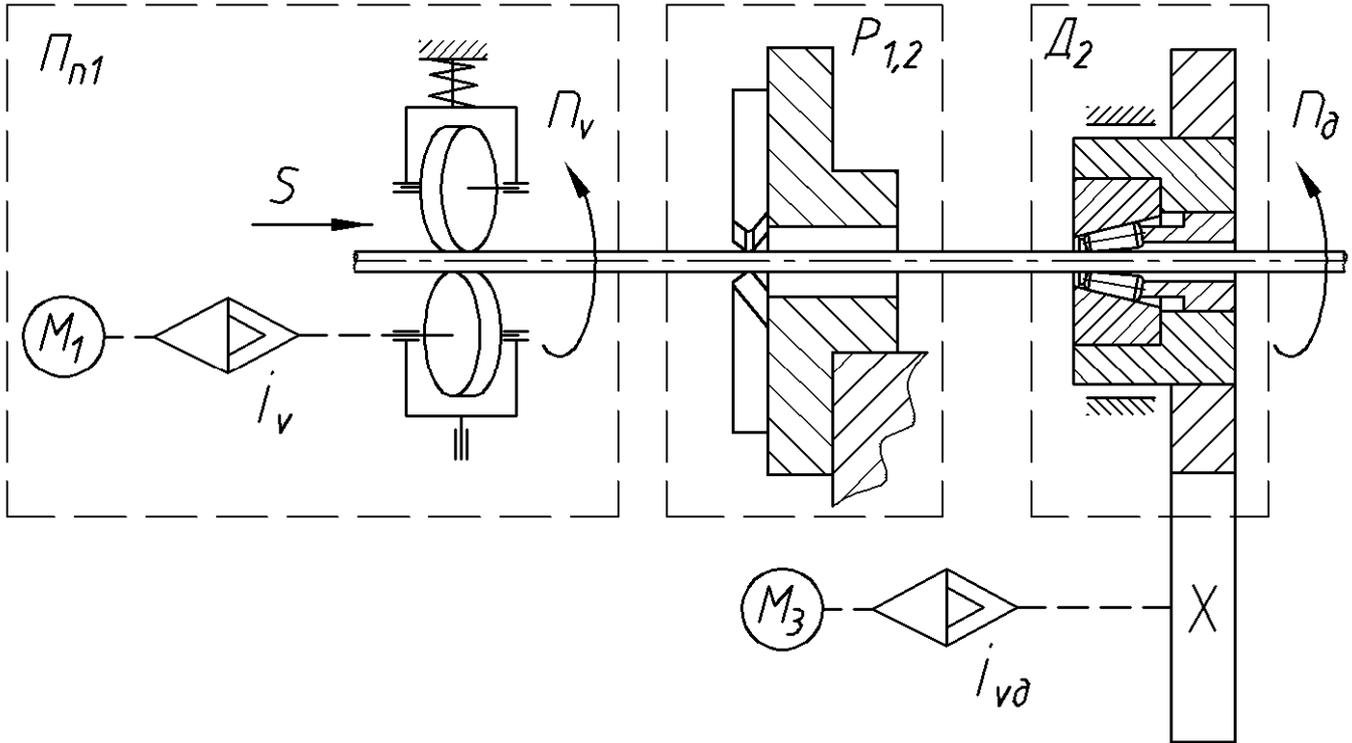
Конструктивная схема совмещенной обработки резанием и ППД роликами с продольно подаваемой и вращаемой заготовкой в сочетании с неподвижной резцовой головкой и обкатником обеспечивающем самоподачу заготовки
